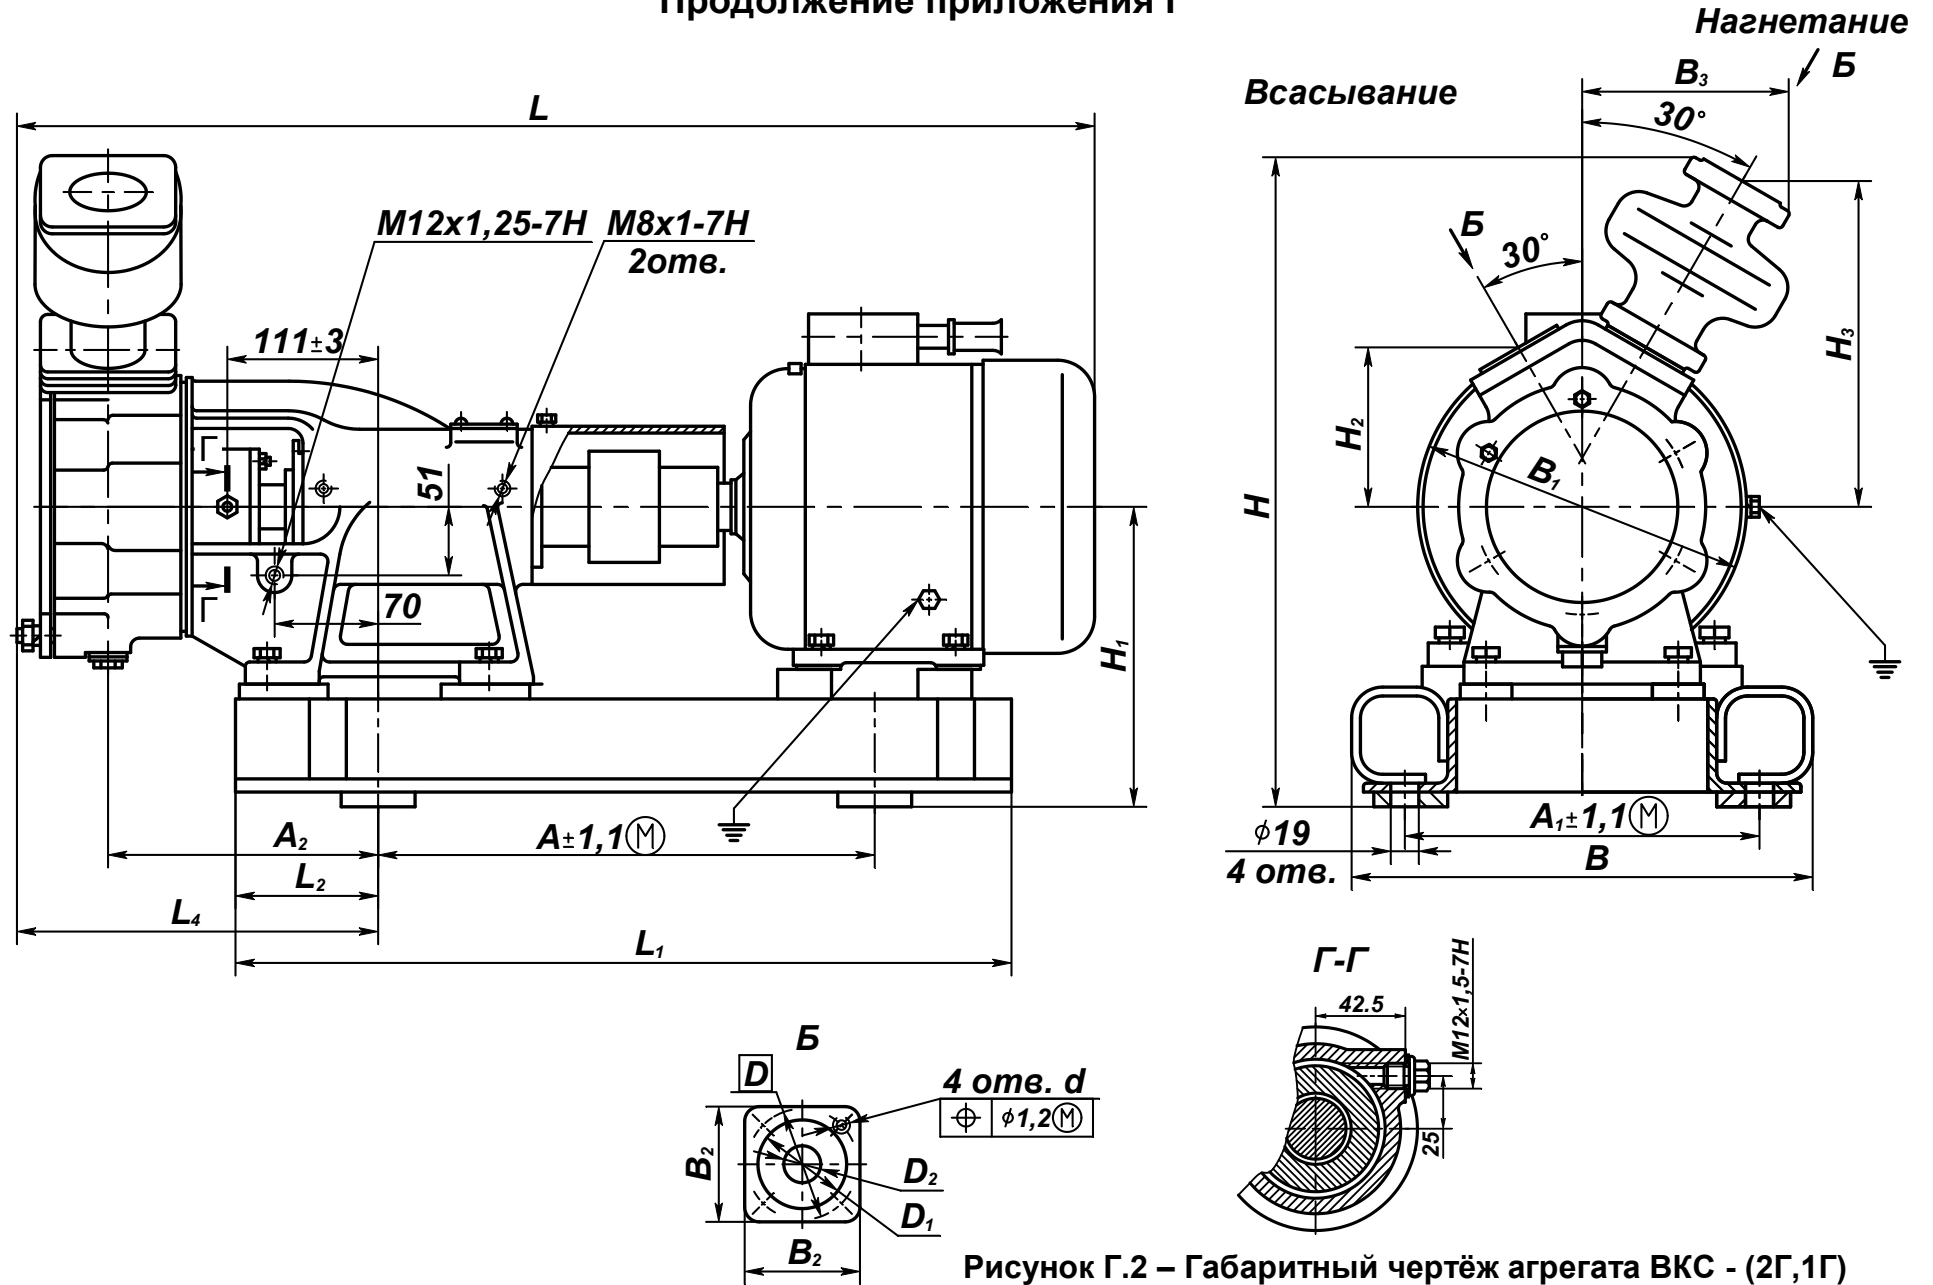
Габаритный чертёж агрегата ВКС - (2Г,1Г)
